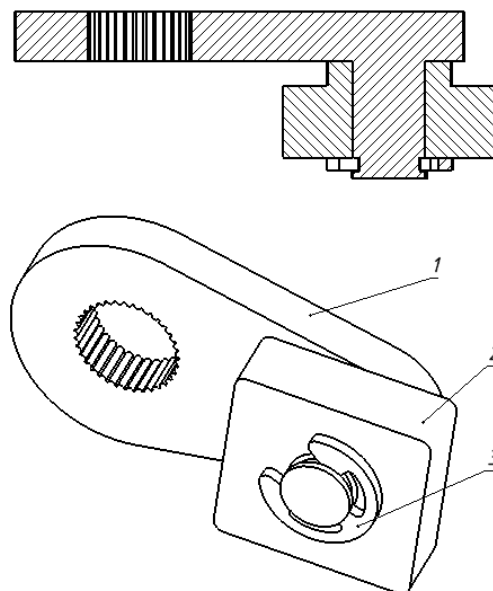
Механізм переміщення головки для малювання за допомогою сервоприводу
